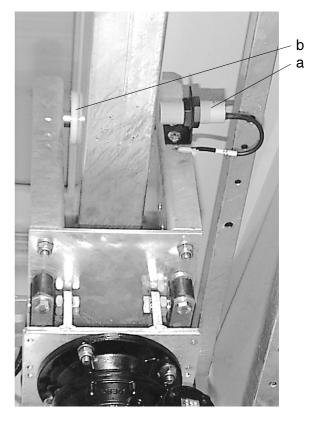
Тележка с боковыми щетками (вид снизу) а Конечный выключатель боковой щетки b Ходовые ролики
